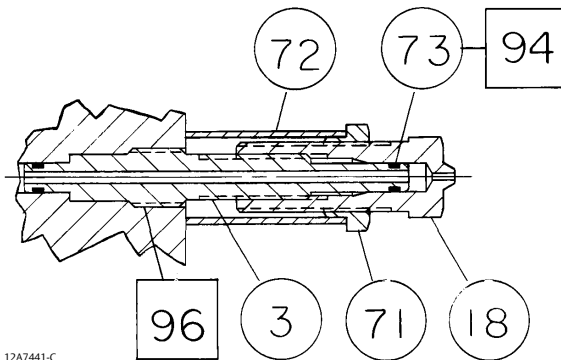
Desenho do Conjunto do Posicionador 3582 da Fisher
